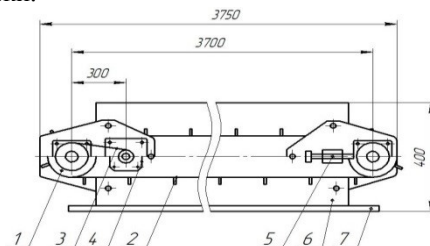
Транспортер загрузочный, схема: 1 – Барабан, 2 – лента транспортная, 3 – зубчатый ремень, 4 – двигатель шаговый, 5 – устройство натяжное, 6 – борт, 7 – рама.
